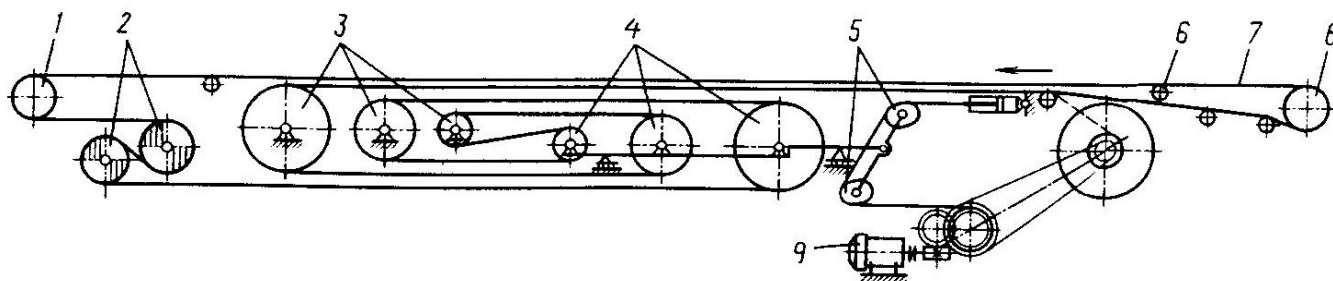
Схема телескопічного стрічкового конвеєра:
